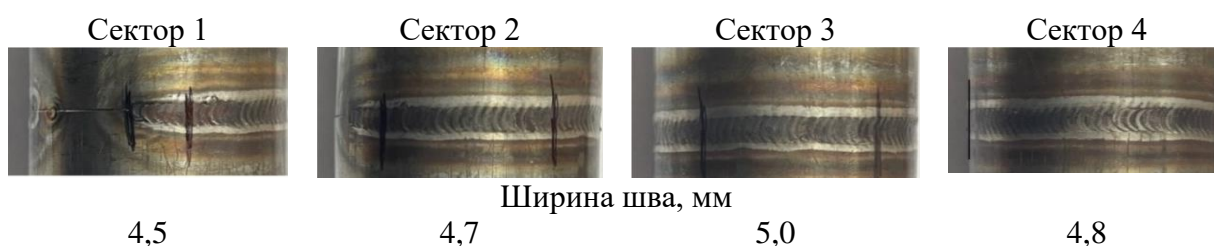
Внешний вид полученного сварного соединения
